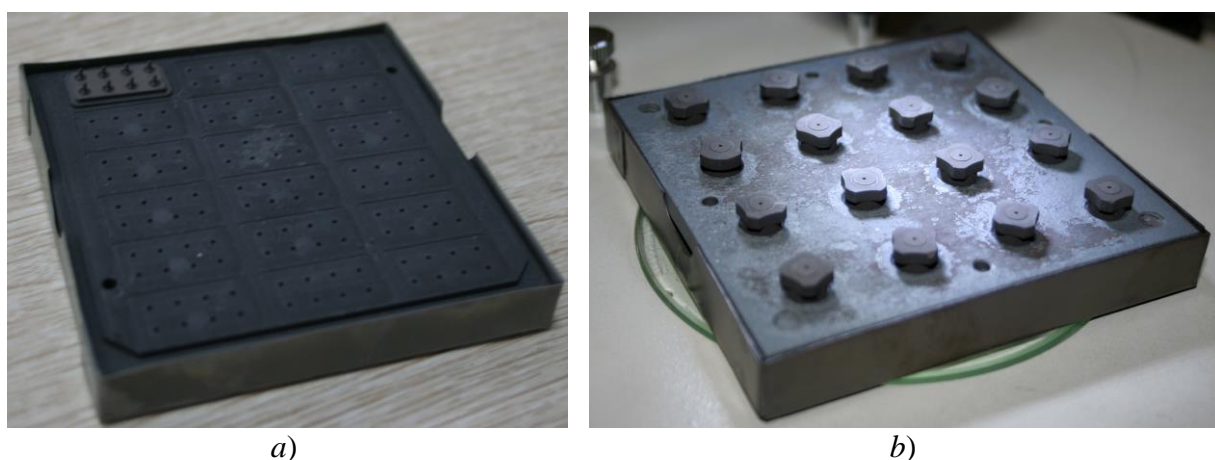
Приспособления для ориентации деталей при спаивании: *a* – цоколя (снята верхняя крышка), *b* – вилки СРГ (показана пластина с установленными опорами)
